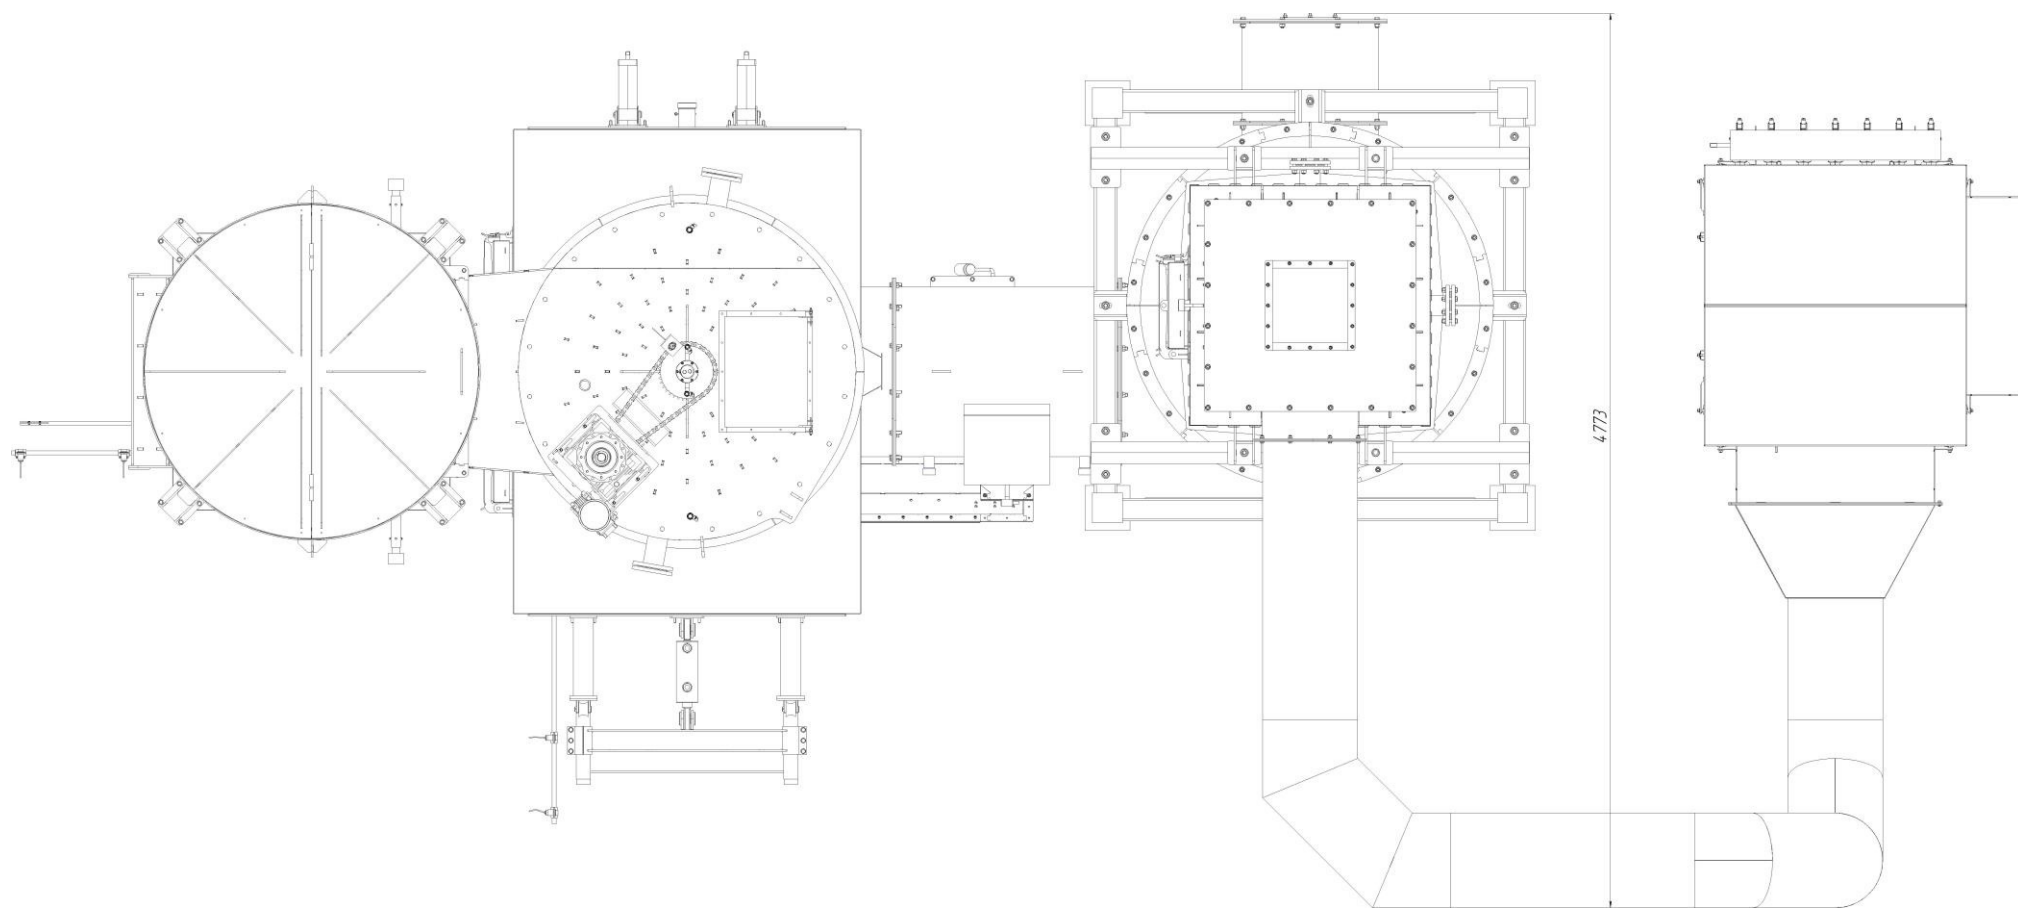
Установка ГГУ – КВ 2,0, вид сверху.
